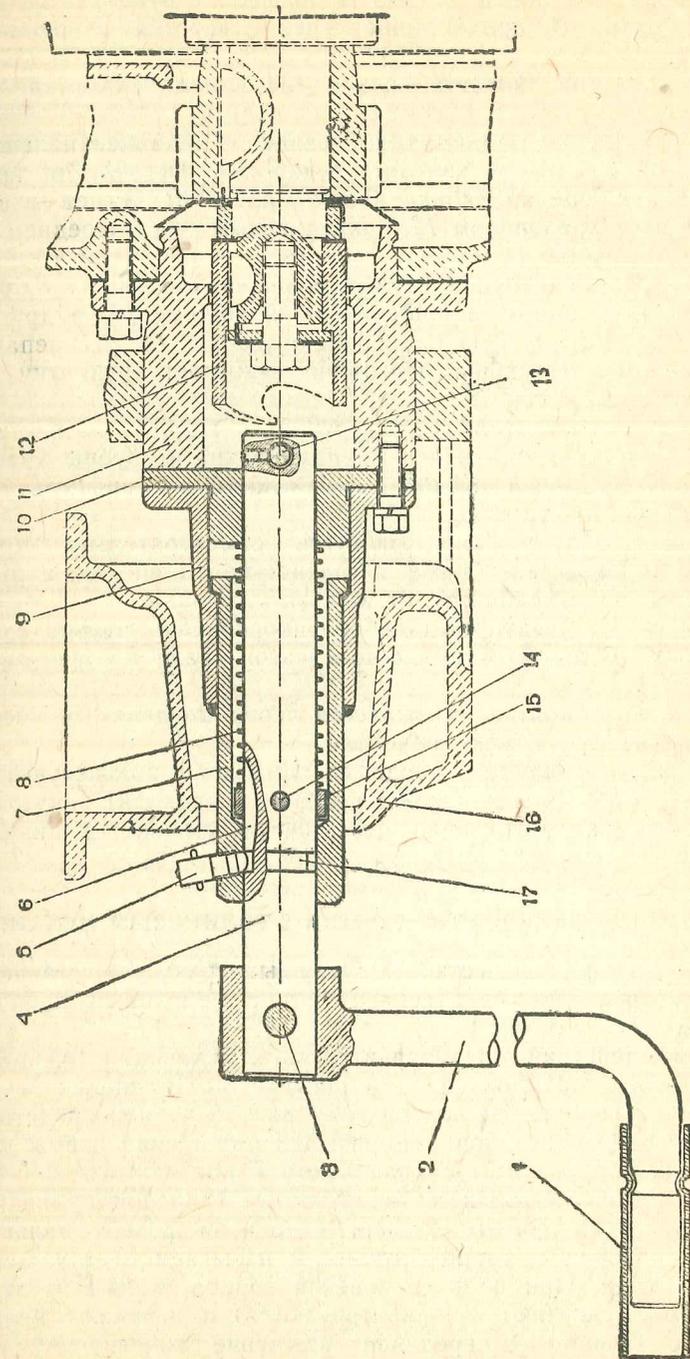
Пусковая рукоятка без предохранительного механизма.
